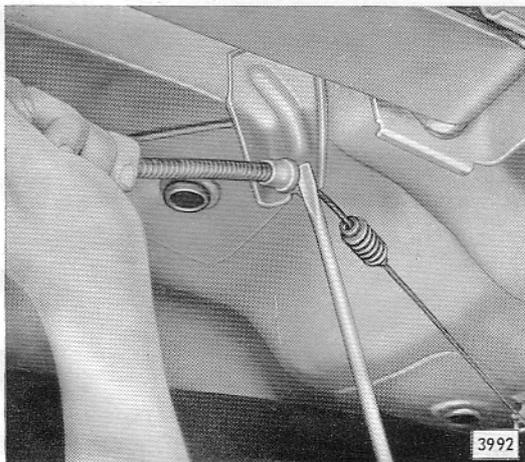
Druckschlauch mit Fassung aus Halter am Wagenboden herausdrücken
